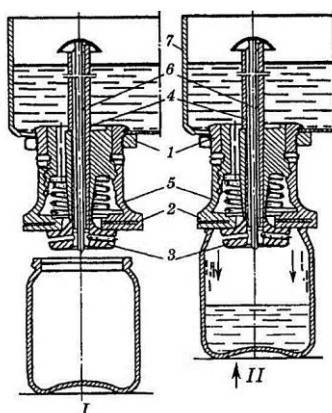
Дозатор за рівнем: I — початок дозування; II — кінець дозування; 1 — корпус; 2 — гумовий патрубок; 3 — сідло-витискувач; 4 — гумовий патрубок; 5 — пружина; 6 — патрубок; 7 — ємність зберігання рідкого харчового продукту
